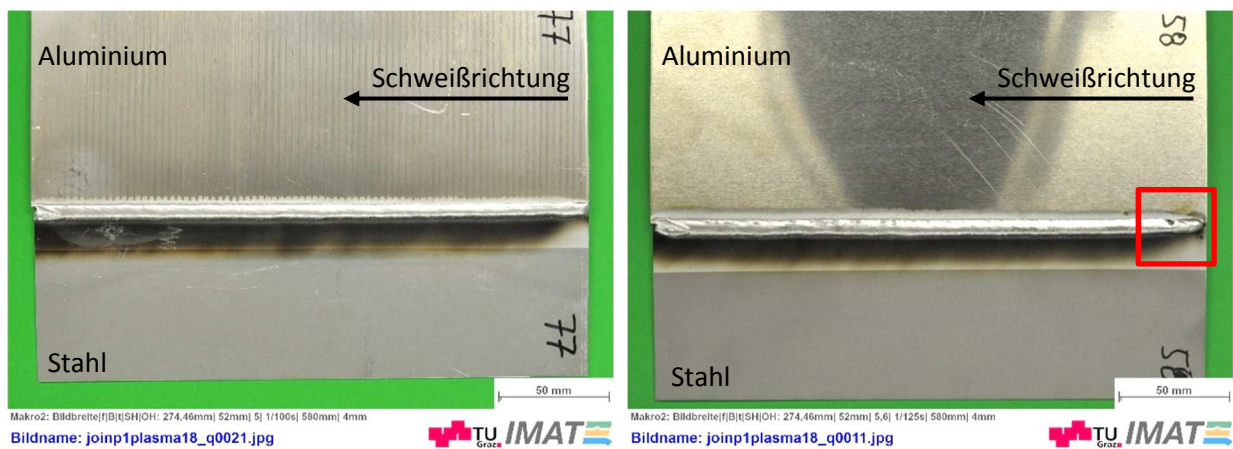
Schweißnähte der Hauptversuche 77 (links) und 58 (rechts); Bindefehler rot markiert
